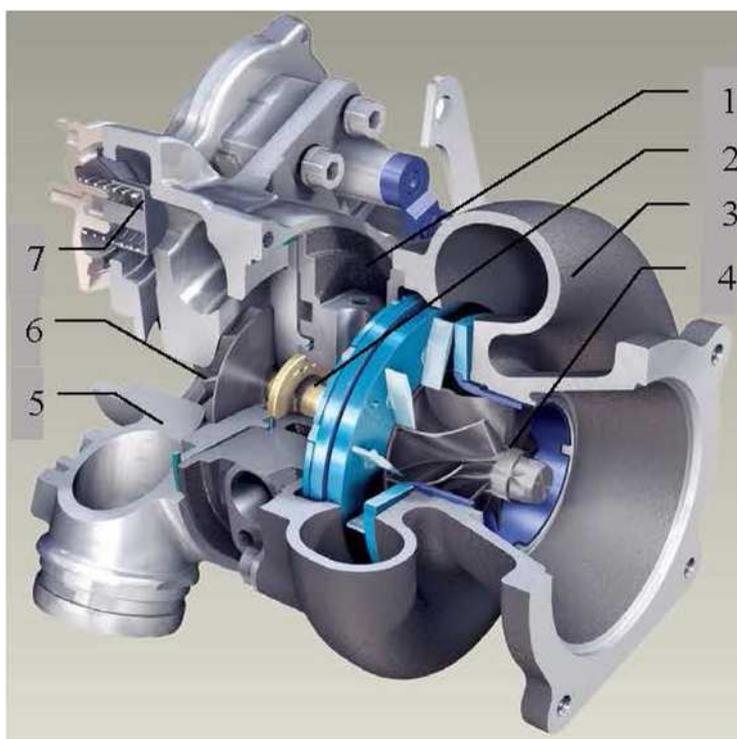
Схема классического турбокомпрессора в разрезе:
